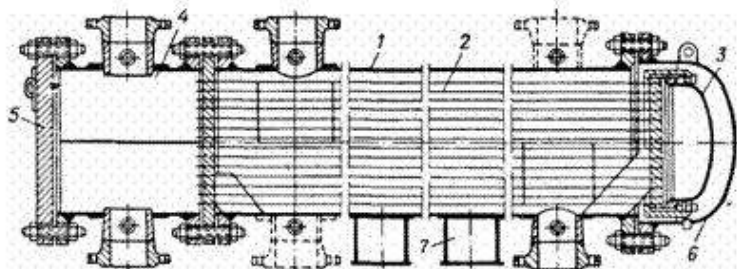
Кожухотрубчатый теплообменник с плавающей головкой: 1 – корпус, 2 – трубный пучок, 3 – плавающая головка, 4 – распределительная камера, 5 – крышка, 6 – днище, 7 – опора
